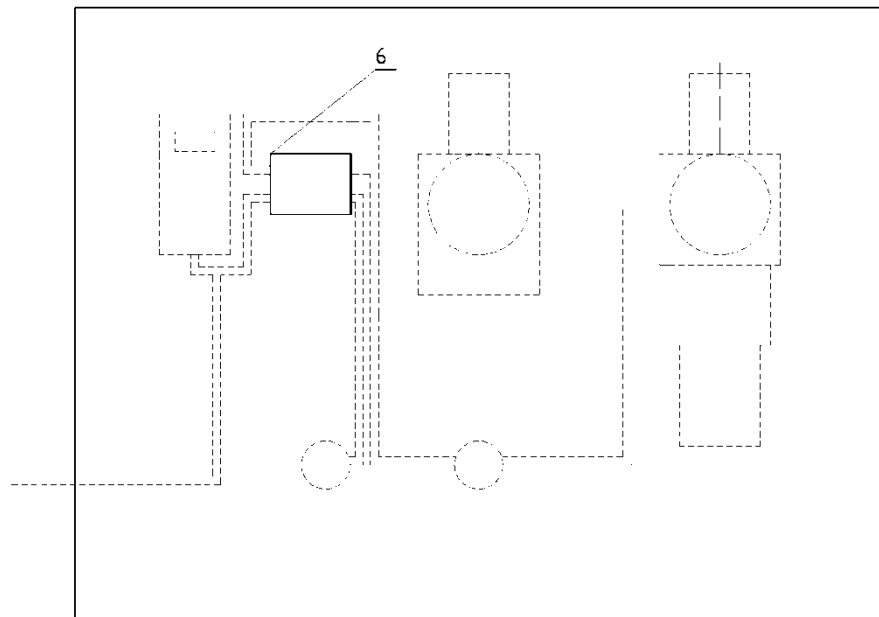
Schematické zobrazení konzoly se součástkami (nárys)
